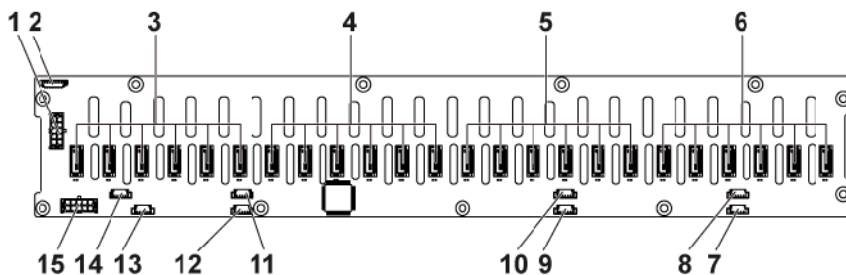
Vue arrière du fond de panier de disque dur de 2,5 pouces
